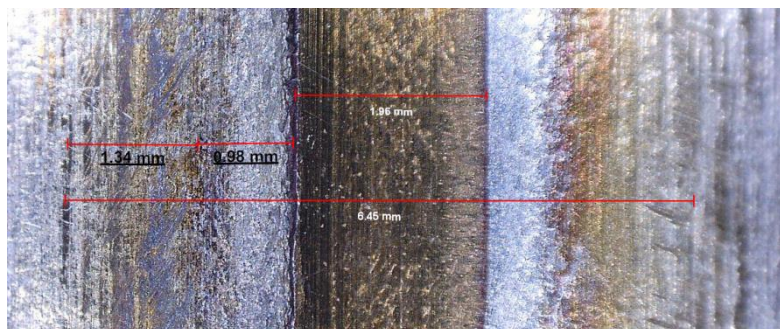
Material base de soldadura láser 100X, ataque vilella
